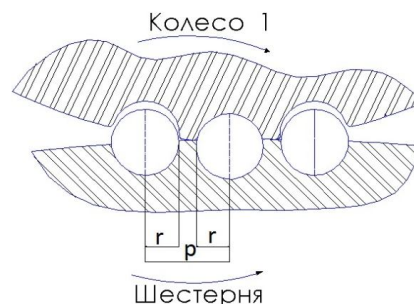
Зацепление колеса и шестерни вид спереди (разрез)
